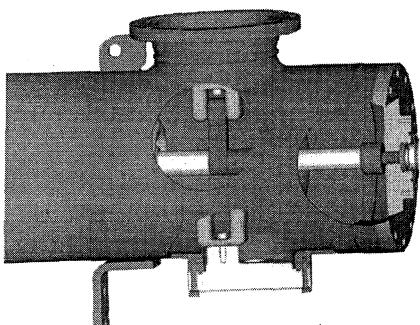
Комбинированный разъединитель-заземлитель ячейки PASS MO с одной системой шин (подвижный контакт подключен к сборнойшине)
